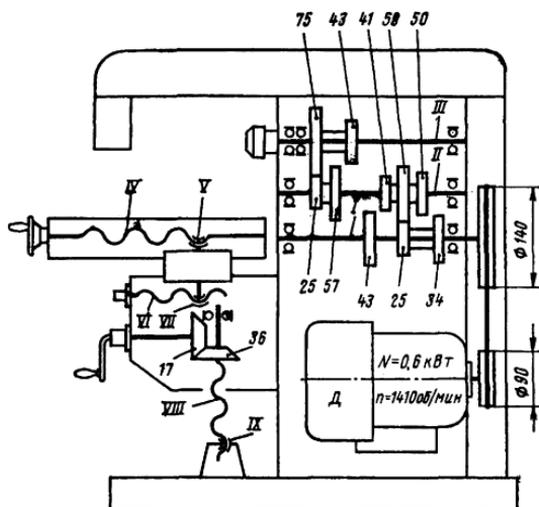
Кинематическая схема горизонтально-фрезерного станка НГФ-110Ш
